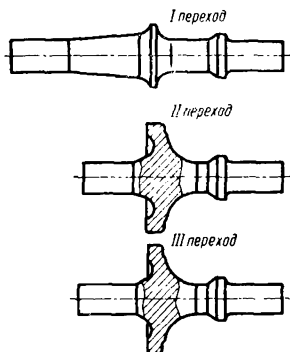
Переходы штамповки поковки, требующей штампа со скользящими вставками
